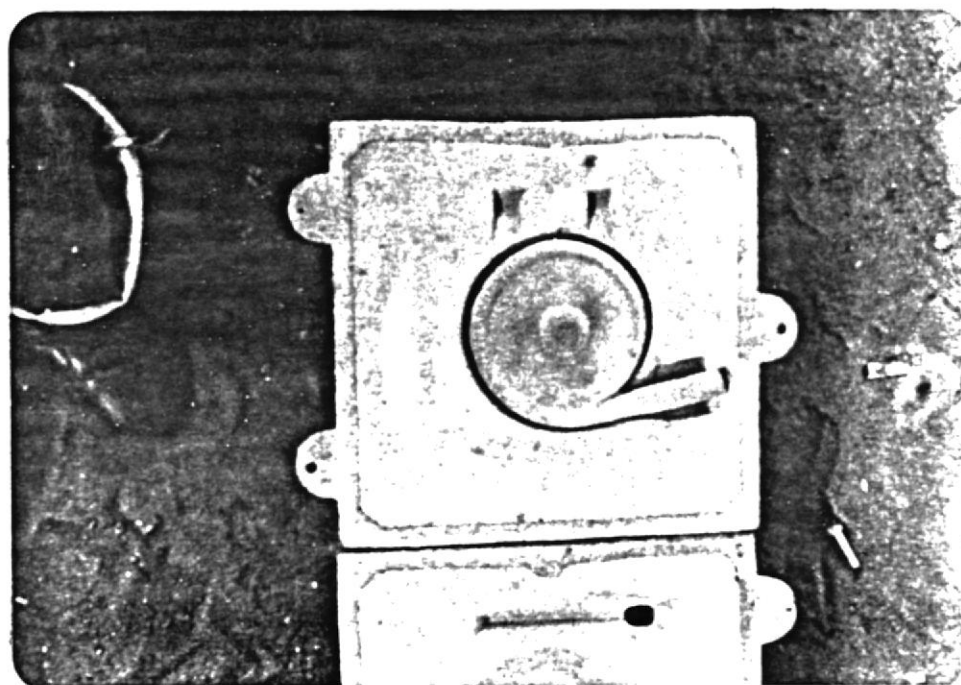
Corazón ensamblado en el fondo del Molde
